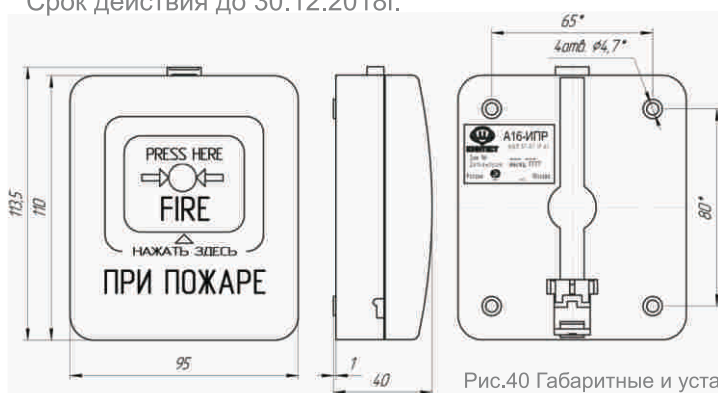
Габаритные и установочные размеры адресного ручного извещателя.
